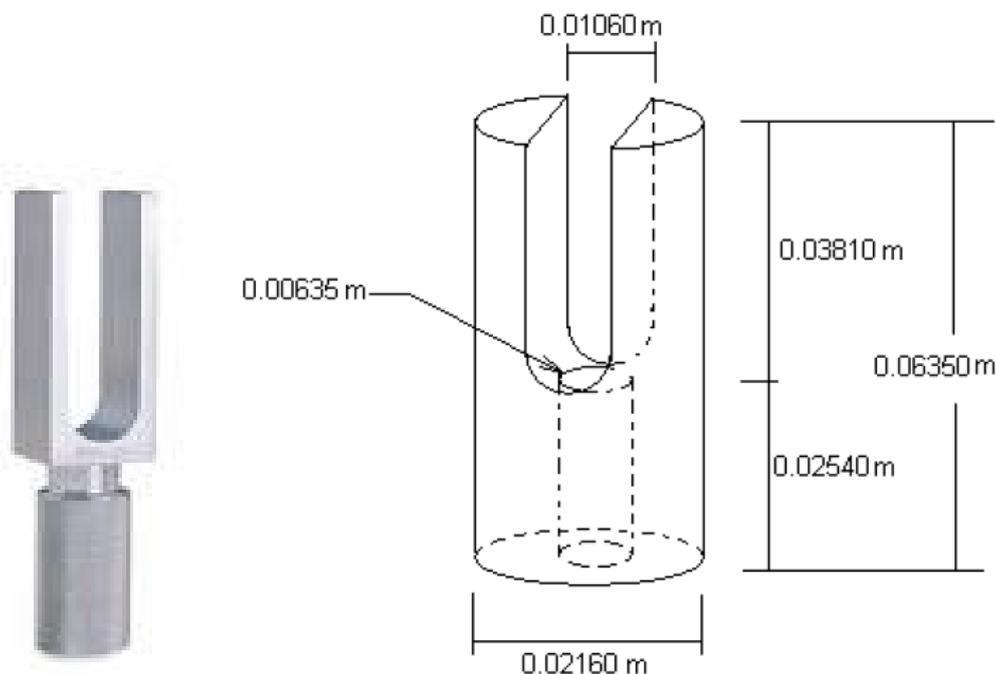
Foto de um diapasão e modelo a ser construído com dimensões em metros.
